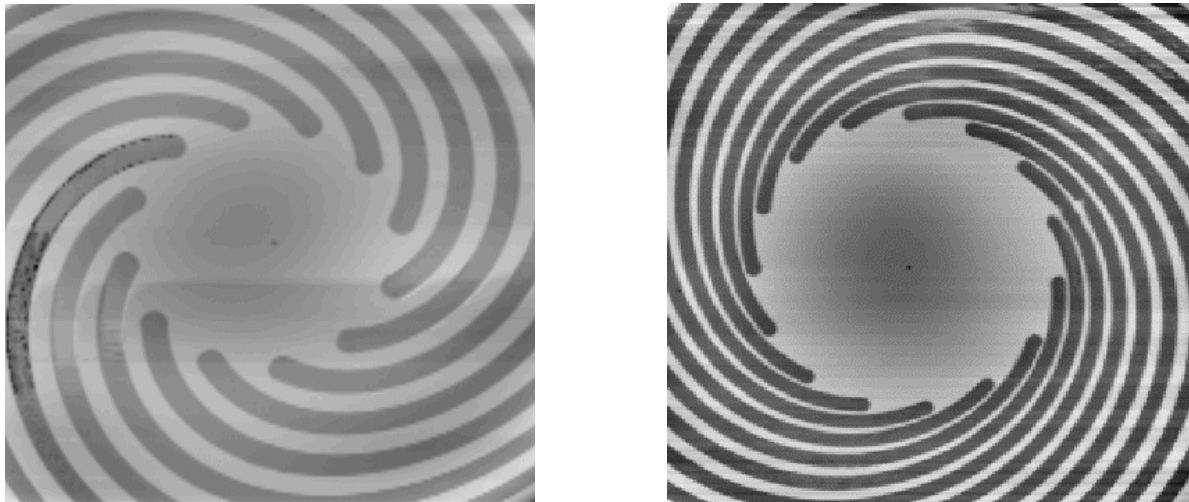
Originaldarstellung einer strukturierten Lagerfläche
